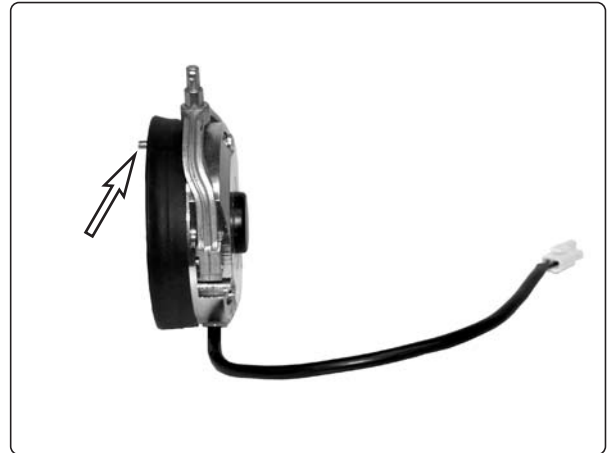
Teile mit einer der Befestigungsschrauben aufeinander ausrichten. Gummidichtung einsetzen.
